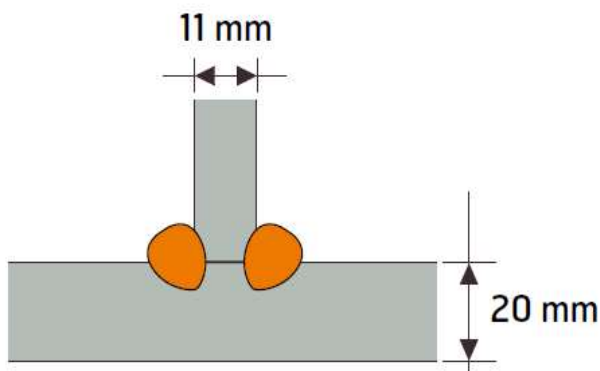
Efeito do aporte de calor em uma junta soldada.
